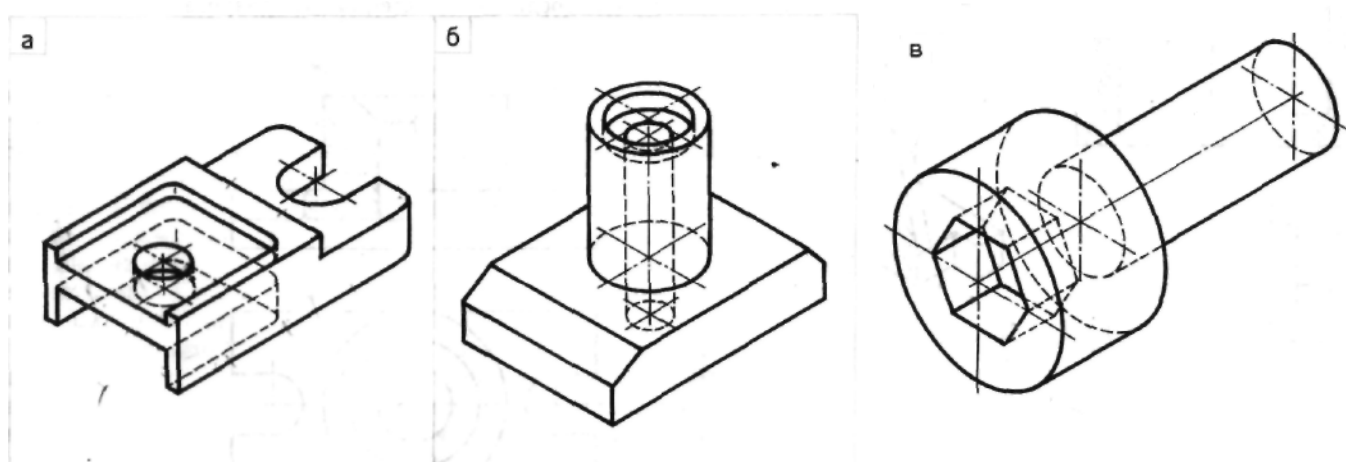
Детали: а — «Плита»; б — «Опора»; в — «Ключ»
